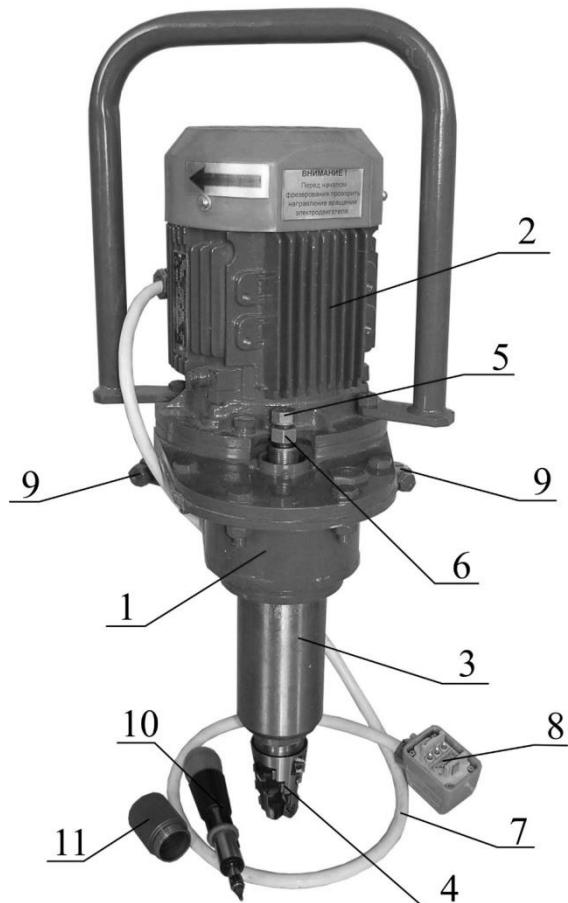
Общий вид фрезерной головки станочного модуля МФ-024: 1- корпус; 2- электродвигатель; 3 - шпиндельный узел; 4 - наборная профильная фреза с твердосплавными пластинами; 5 - шомпол для затяжки фрезы в шпинделе; 6 - гайка; 7 - кабель; 8 - разъем подключения к блоку магнитных пускателей; 9 - зажим клеммный с болтом и гайкой; 10 - отвертка для установки пластин фрезы; 11 - предохранительная крышка шомполя
